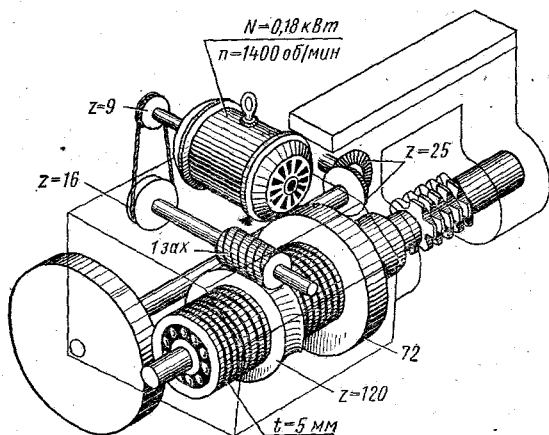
Механизм периодического осевого перемещения червячной фрезы зубофрезерного станка мод. 5Е32
